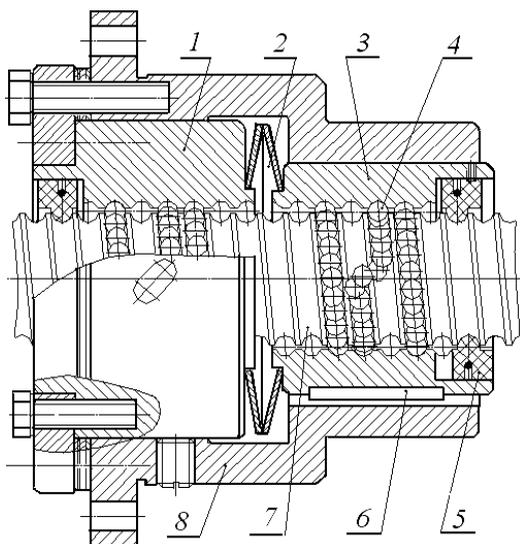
Передача винт-гайка качения с осевым смещением гайки 3 под действием пружины 2 для регулирования натяга при фиксированной второй гайке 1 в корпусе 8
